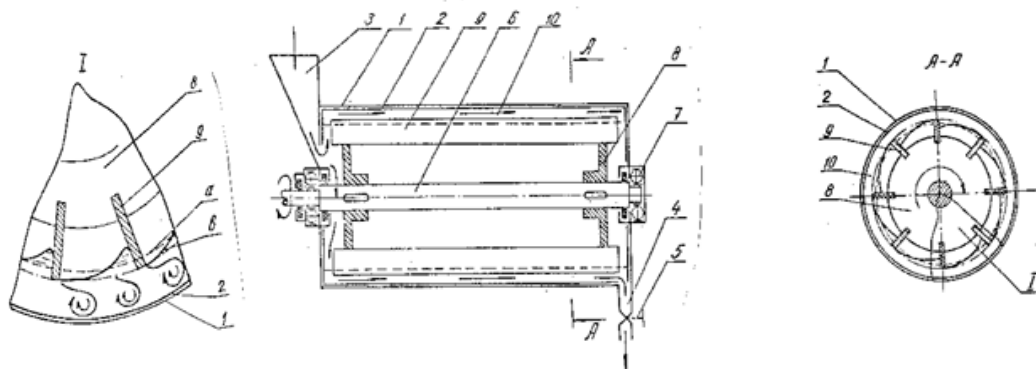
Схема лопастного механоактиватора “ЛМА-2М”
